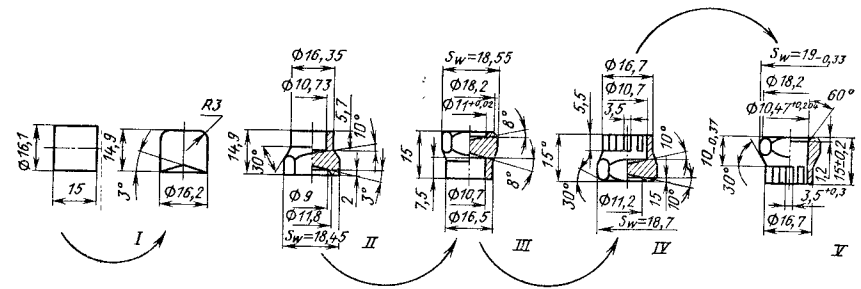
Технологический процесс штамповки корончатой гайки М12×1,25 на пятипозиционном автомате
